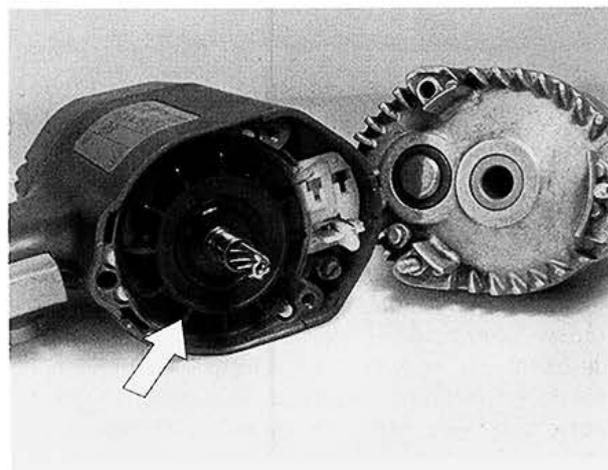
Handbohrmaschine mit Radiallüfter
